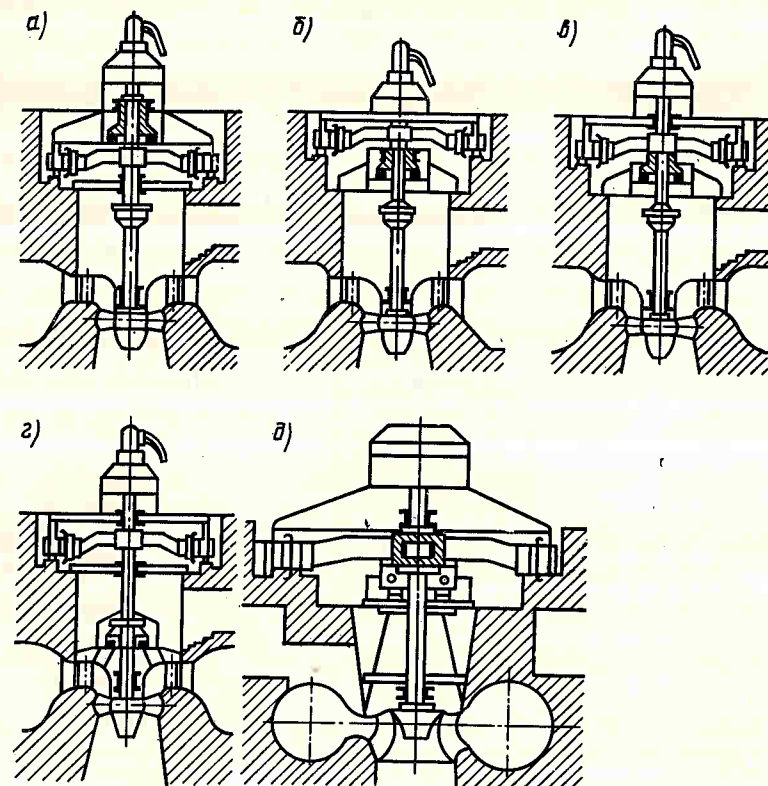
Компонировки гидроагрегатов с различным расположением направляющих подшипников гидрогенератора
